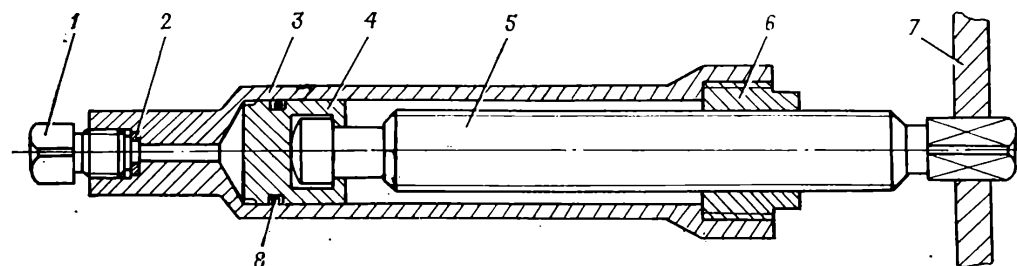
Установка приспособления 41.020 Сб для оттягивания поршня компенсатора:
